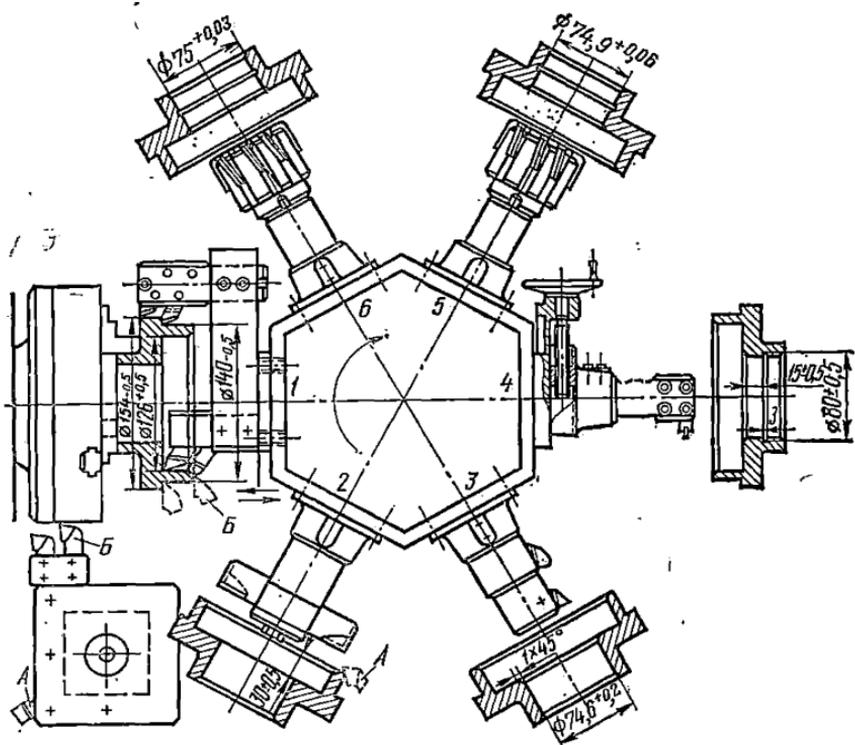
Наладка токарно-револьверного станка для обработки заготовки зубчатого колеса.
